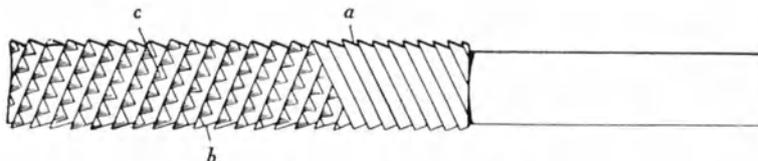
Rundfeile mit gewindeartigen Zähnen.
